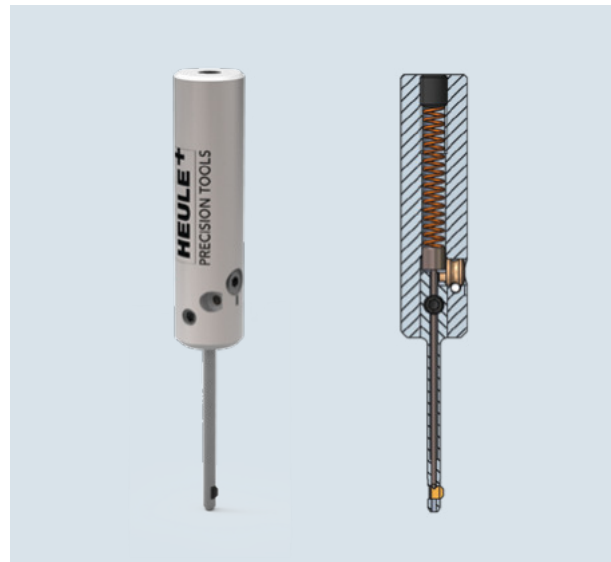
Der konstruktive Aufbau des Werkzeuggehäuses besteht dimensionsbedingt aus zwei Bauteilen: einem Grundkörper und einem Messergehäuse.
